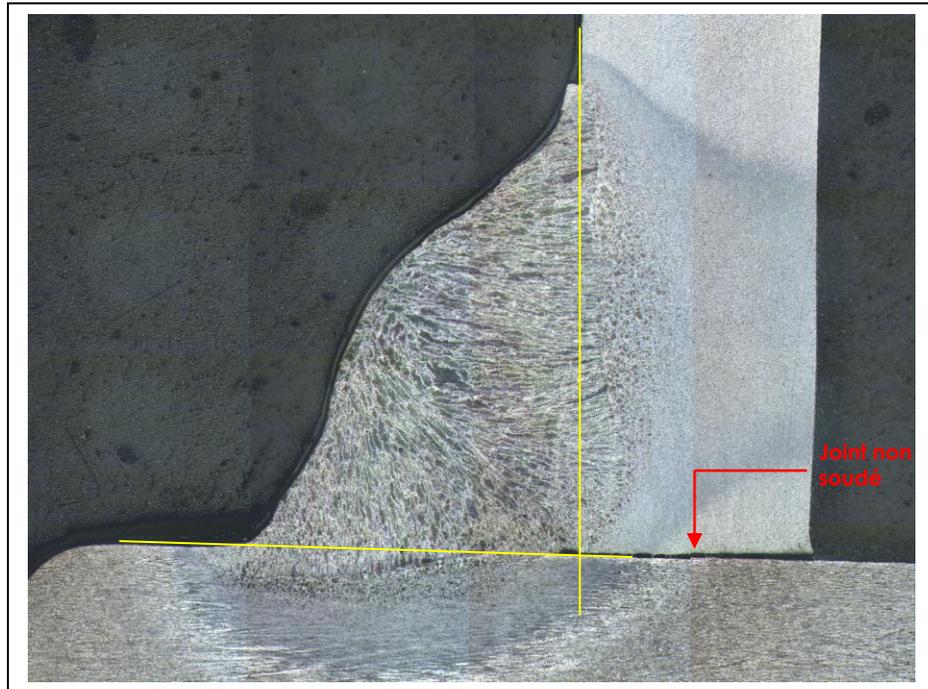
Absence de fissure du cordon de soudure 2GE - surface ext.
